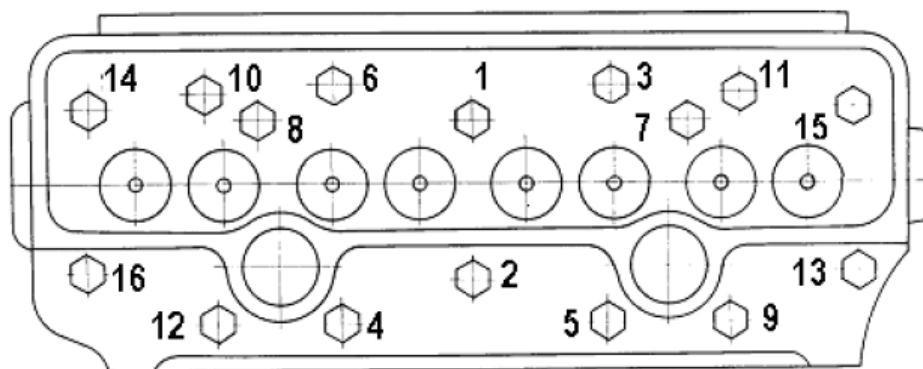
Схема последовательности затяжки болтов крепления головки цилиндров
